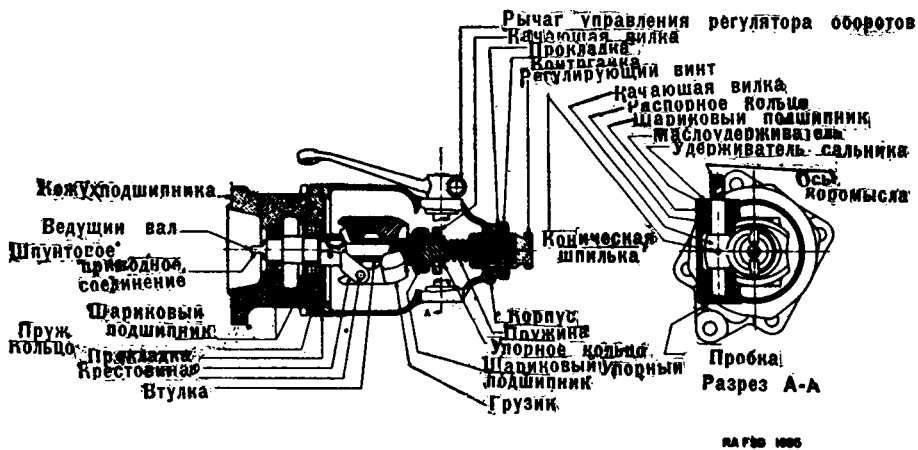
Регулятор оборотов двигателя дизель “Гуильберсон”.
